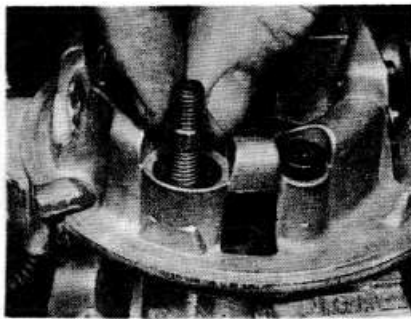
Снимите втулки на шпильках коллектора — двигатель с одноточечным впрыском топлива
